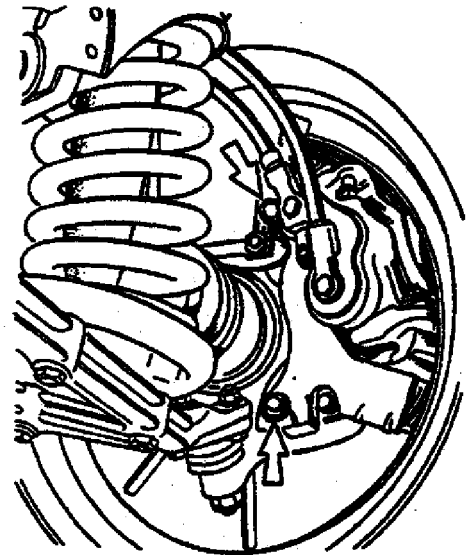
Fixação do freio dianteiro: As setas indicam os parafusos de fixação do conjunto do freio.
